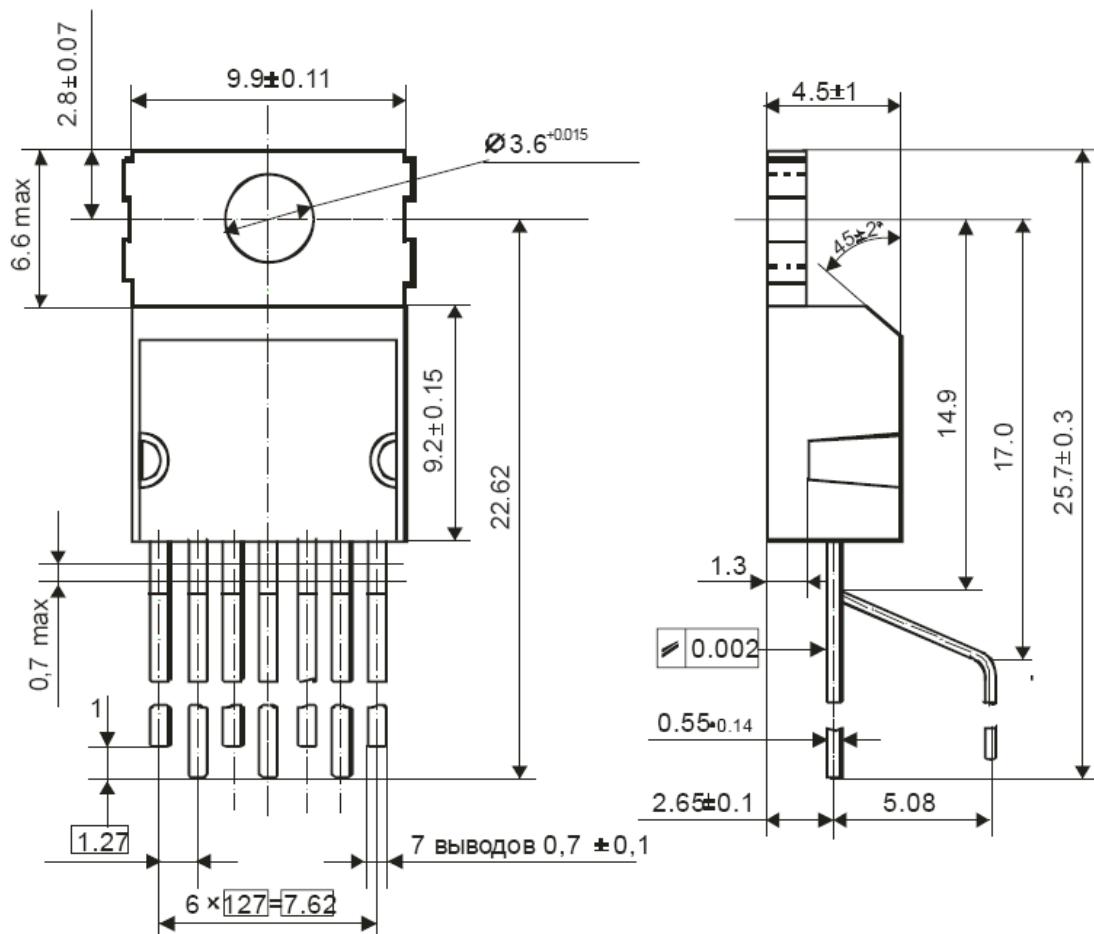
Габаритный чертеж корпуса 1505Ю.7-А (ТО-220АВ/7)
